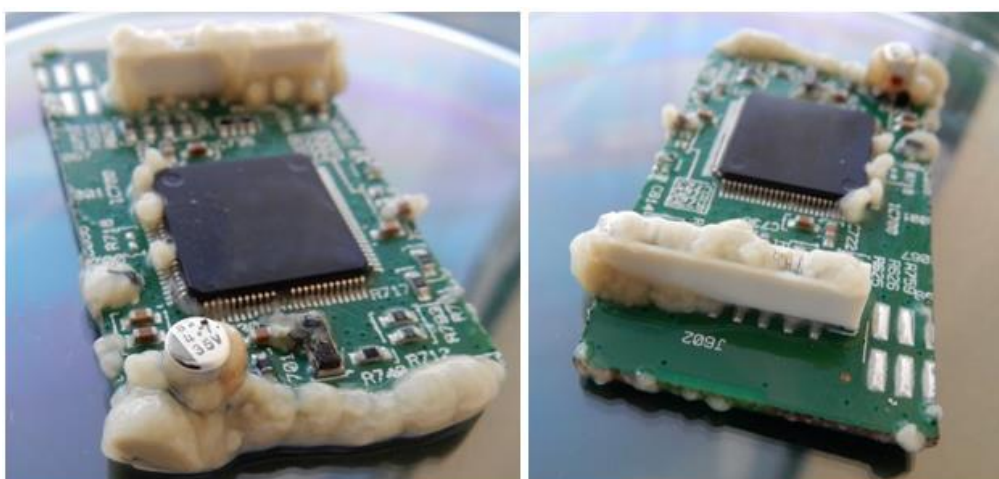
Placa PCB após 33 dias de ensaio.
